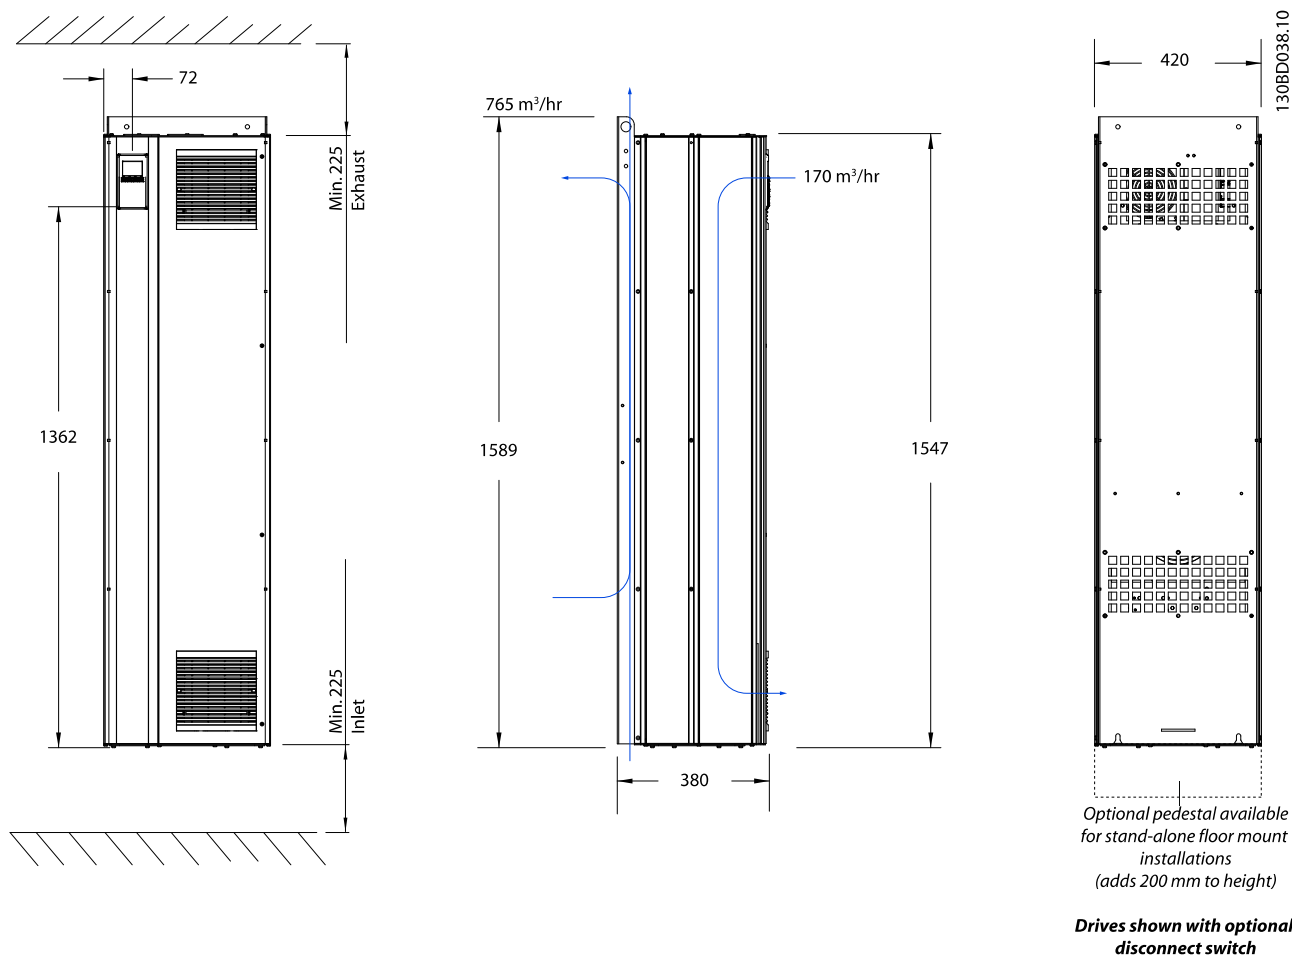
Gerätegröße 42 (Boden- oder Schaltschrankbefestigung)
